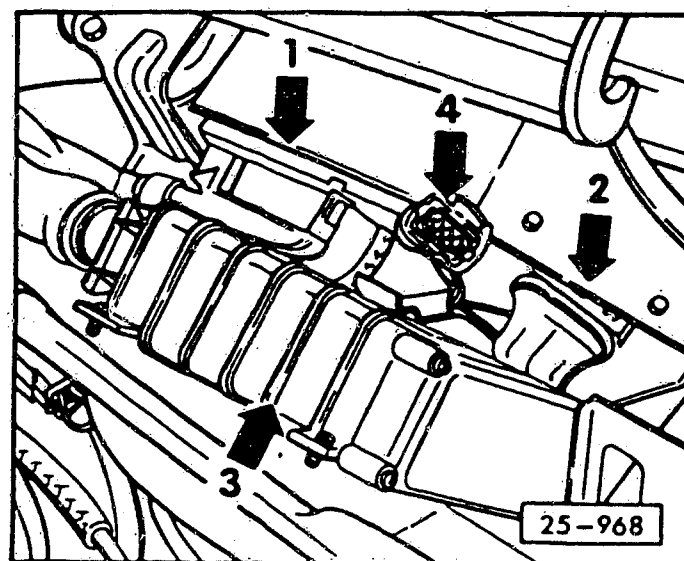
Das Steuergerät ist im Wasserkasten eingebaut. 1 VEZ-Steuergerät – 2 TSZ-H-Schaltgerät – 3 KE-Jetronic-Steuergerät – 4 Anschlussstecker für Höhengabe (neu in gewissen Ländern).
